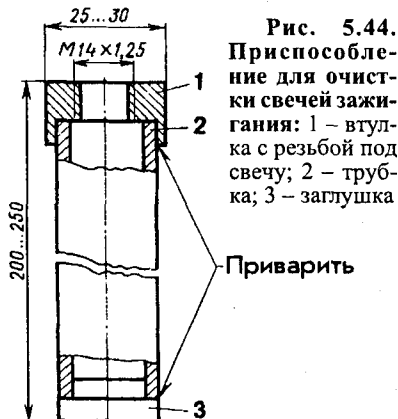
Приспособление для очистки свечей зажигания: 1 – втулка с резьбой под свечу; 2 – трубка; 3 – заглушка
